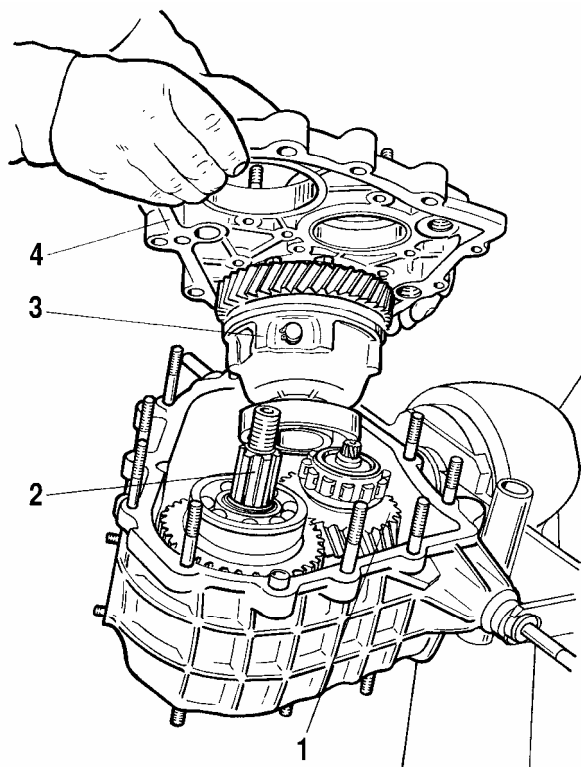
Снятие передней крышки раздаточной коробки:
